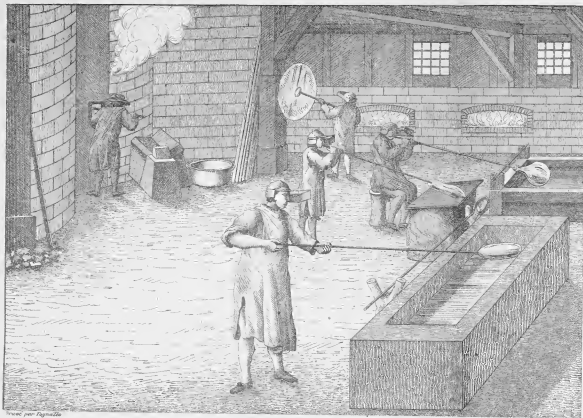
Intérieur d'une halle de verres soufflés (verres en plateaux).
